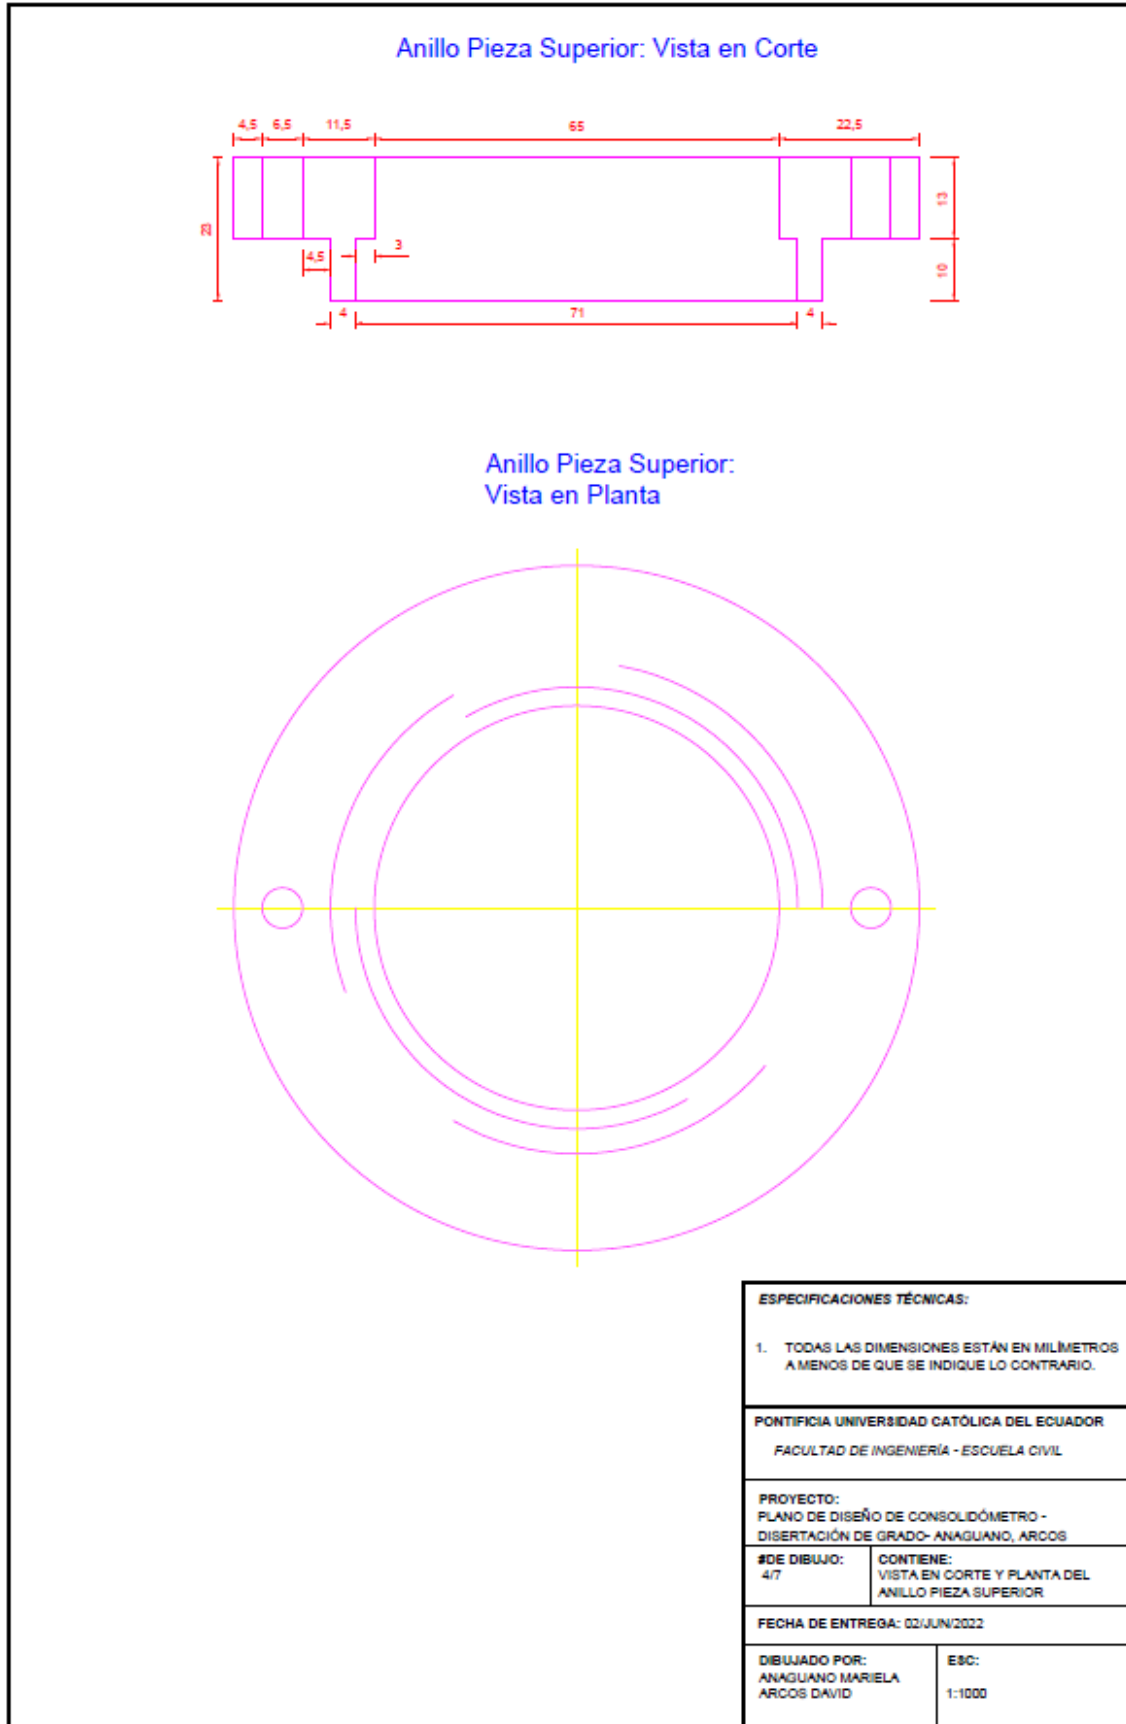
Plano de diseño del consolidómetro. Vista en corte y planta del anillo pieza superior. Elaboración propia.
